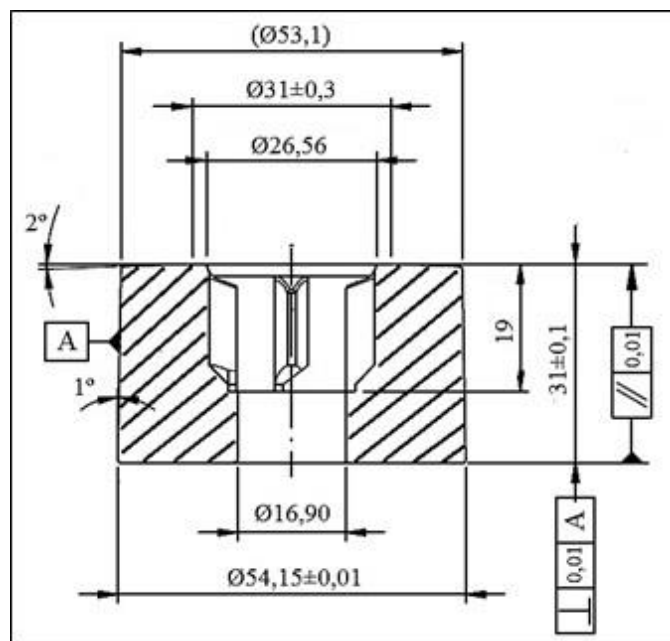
Desenho da matriz MT-3673 para a extrusão de engrenagem.
